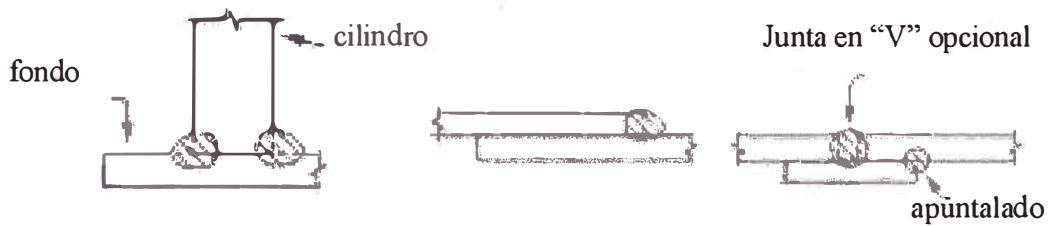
Método para preparar la junta traslapada de las planchas del fondo debajo del cilindro
